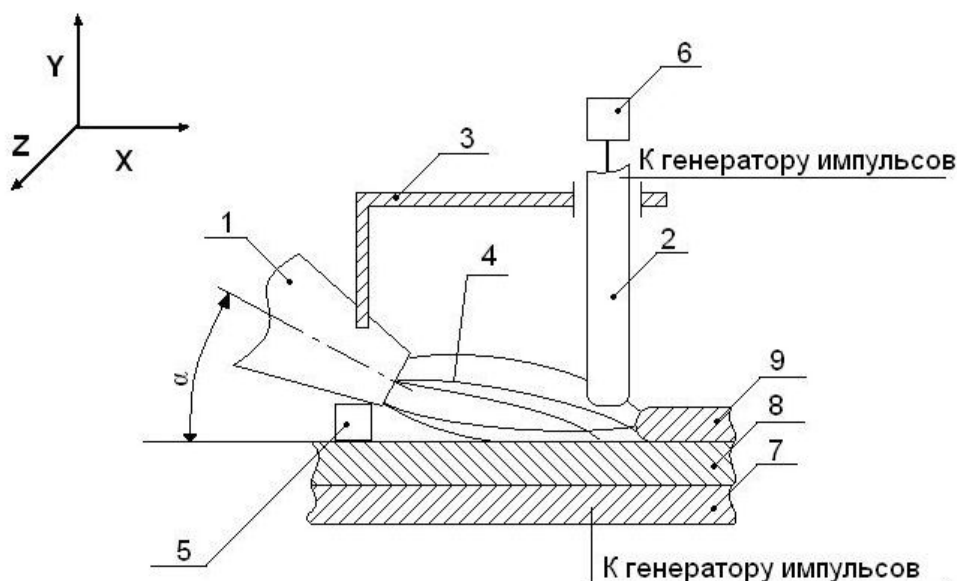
Схема устройства для нанесения покрытий на металлические детали
